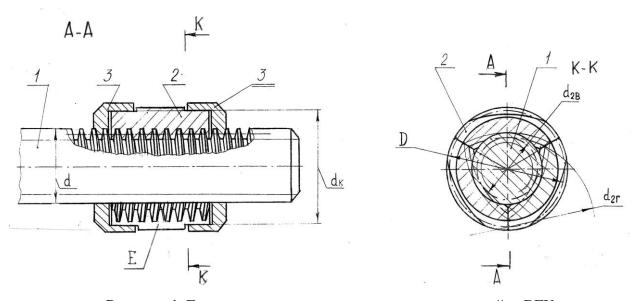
Геометрические параметры передачи винт-гайка ВГК с клиновым зазором в зацеплении.
